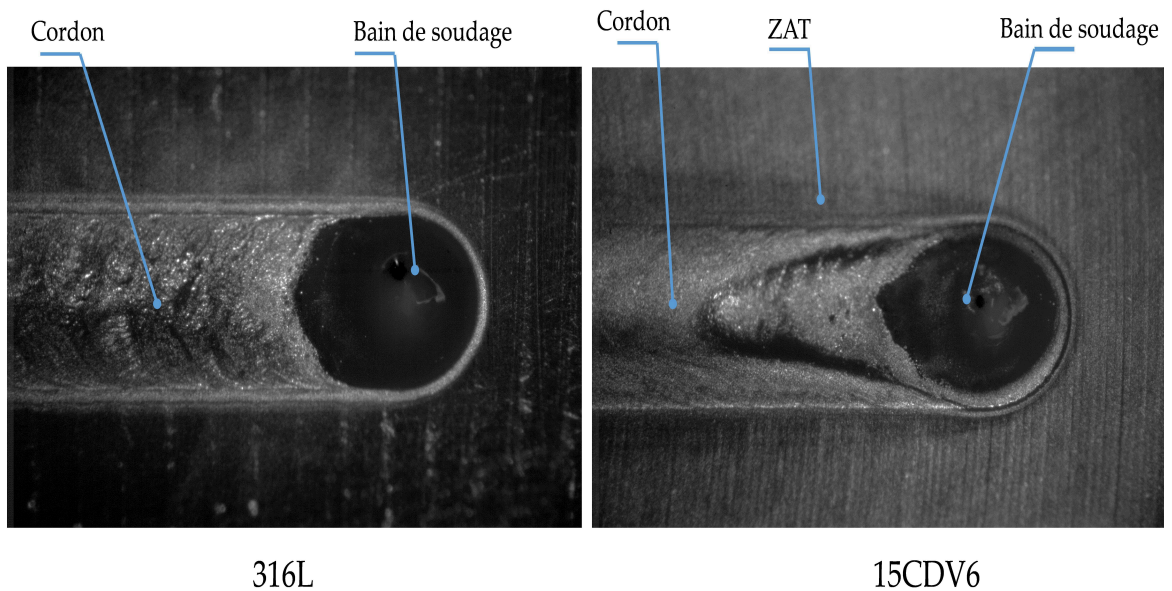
Morphologie du bain de soudage des deux matériaux 316L et 15CDV6 pour une vitesse de soudage de $1600 \text{ mm}\cdot\text{min}^{-1}$.
